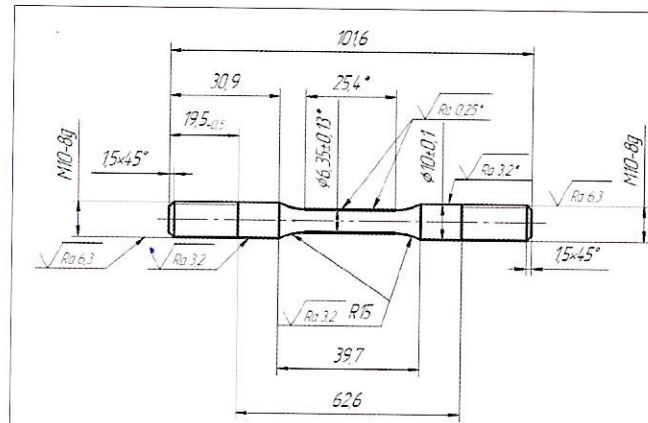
Образец для испытаний на растрескивание под действием напряжения в сульфидсодержащей среде (SSC)
